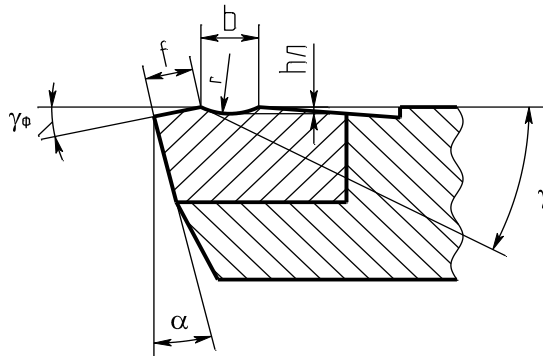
Ескіз форми заточування передньої поверхні різального інструменту
